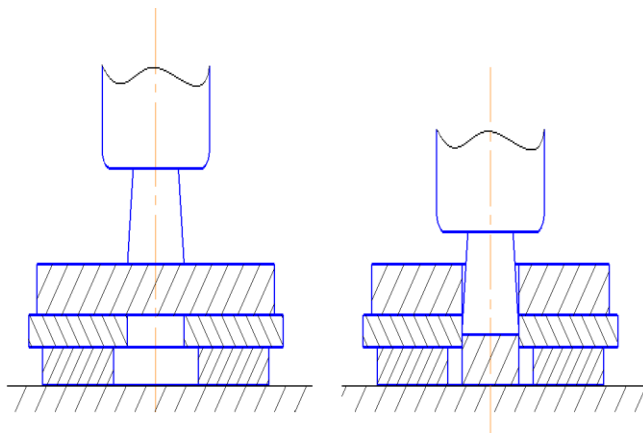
Схема прошивки низких заготовок с подкладным кольцом
